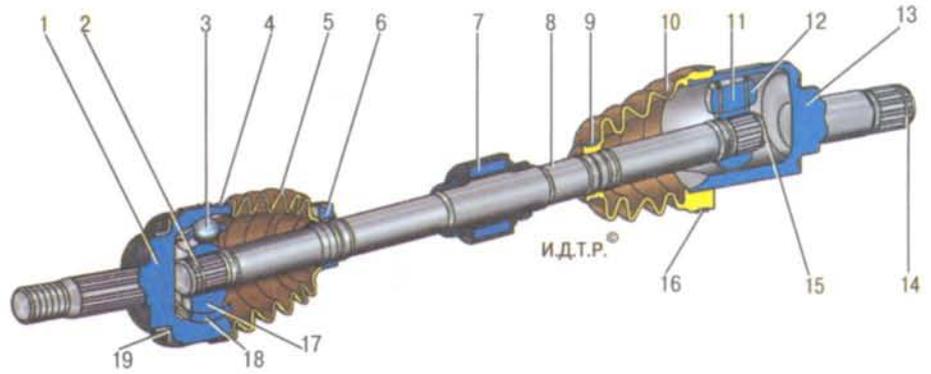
Привод переднего колеса: 1 – корпус наружного шарнира; 2 – стопорное кольцо обоймы наружного шарнира; 3 – шарик наружного шарнира; 4, 6, 9, 16 – хомуты крепления чехла; 5 – чехол наружного шарнира; 7 – динамический демпфер; 8 – вал привода переднего колеса; 10 – чехол внутреннего шарнира; 11 – ступица внутреннего шарнира; 12 – ролик внутреннего шарнира; 13 – корпус внутреннего шарнира; 14 – стопорное кольцо внутреннего шарнира; 15 – стопорное кольцо ступицы внутреннего шарнира; 17 – обойма наружного шарнира; 18 – сепаратор наружного шарнира; 19 – зубчатый венец датчика частоты вращения колеса
